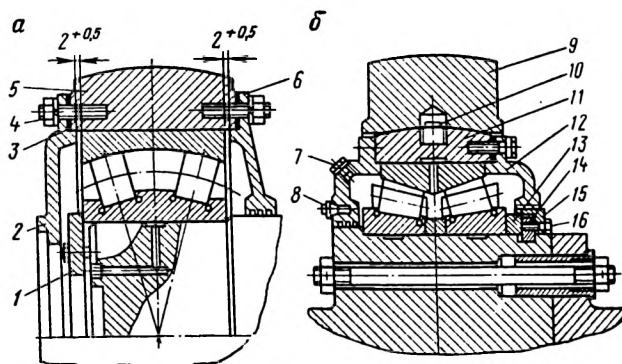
Подшипниковые опоры коренного вала машины МК4×4 со сферическим (а) и коническим (б) подшипниками
